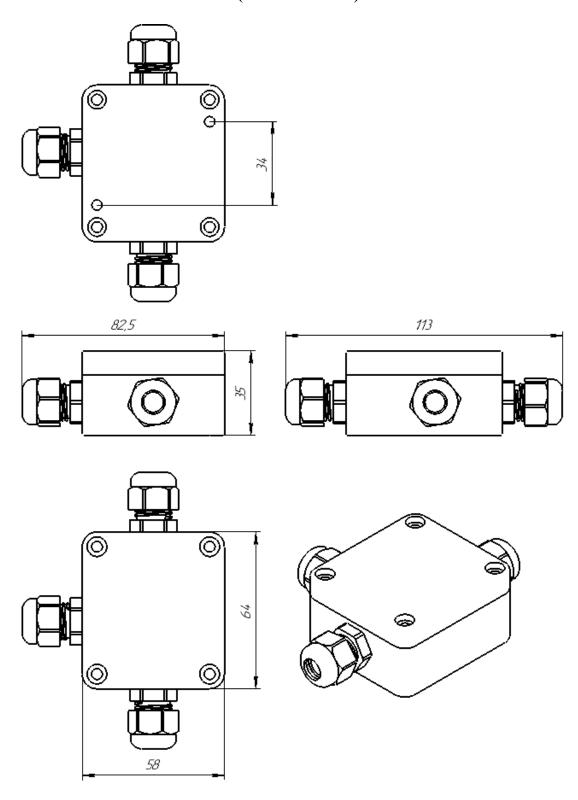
Габаритные и установочные размеры ΠP -3Д ТМ Π
